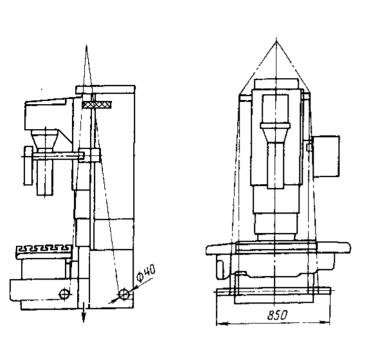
Схема транспортировки станка модели 2E78П в распакованном виде. Масса станка - 2680 кг
